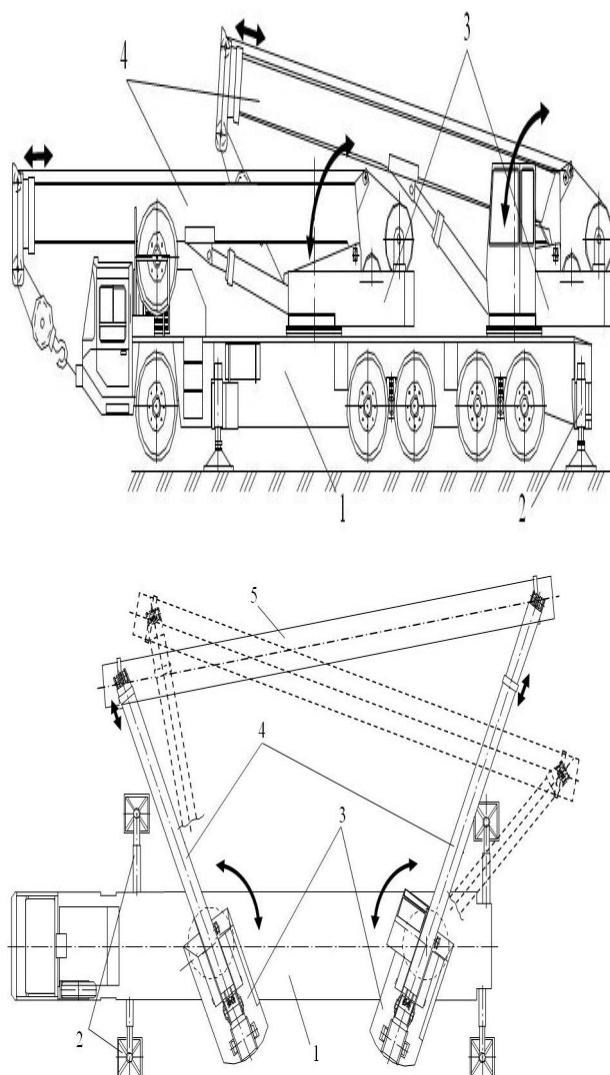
Самоходный двухстреловой ГПК с двумя поворотными платформами (виды сбоку и сверху)
